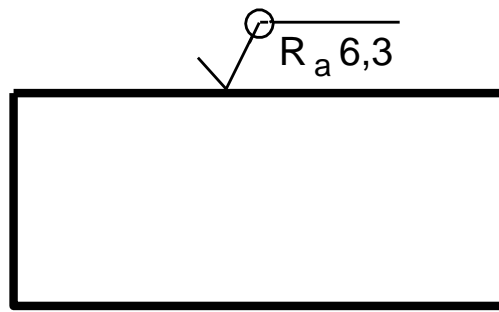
Изображение шероховатости поверхностей, образующих контур
